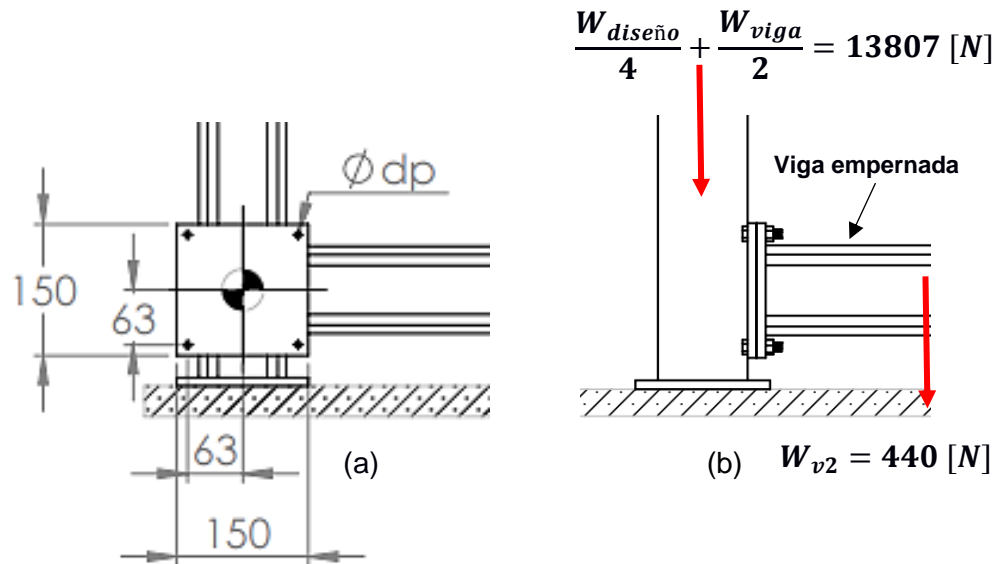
(a) Vista frontal de la posición de los pernos de fijación, (b) Vista lateral de la viga emperrada.
